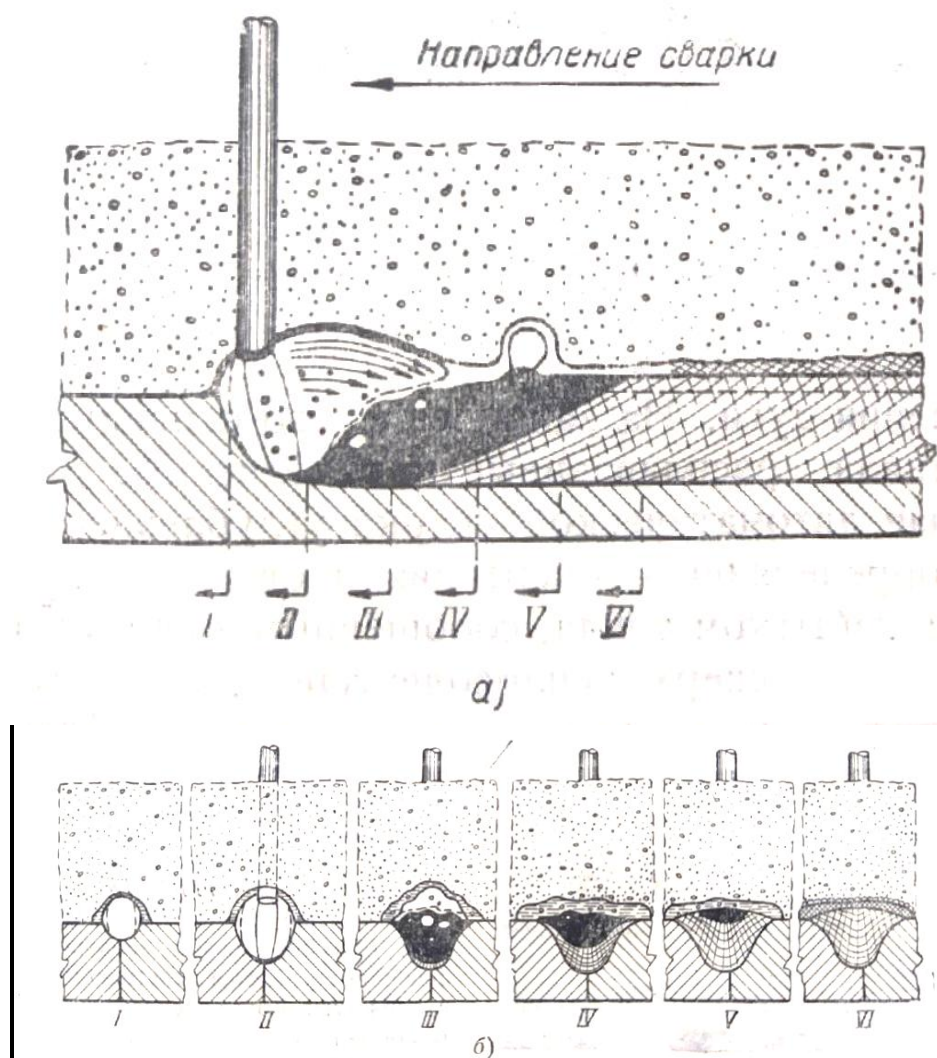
Схема процесса автоматической сварки под флюсом [1]
